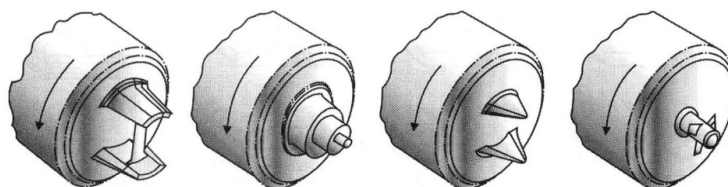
Варіанти конструктивного виконання зварювального інструмента для ЗТП
